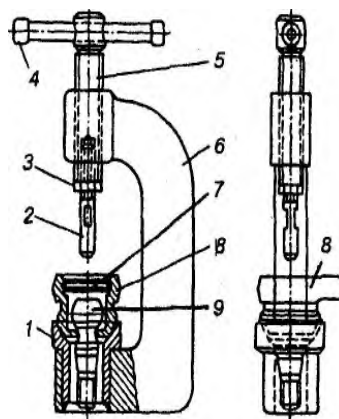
Приспособление для сборки шарниров рулевых тяг:
